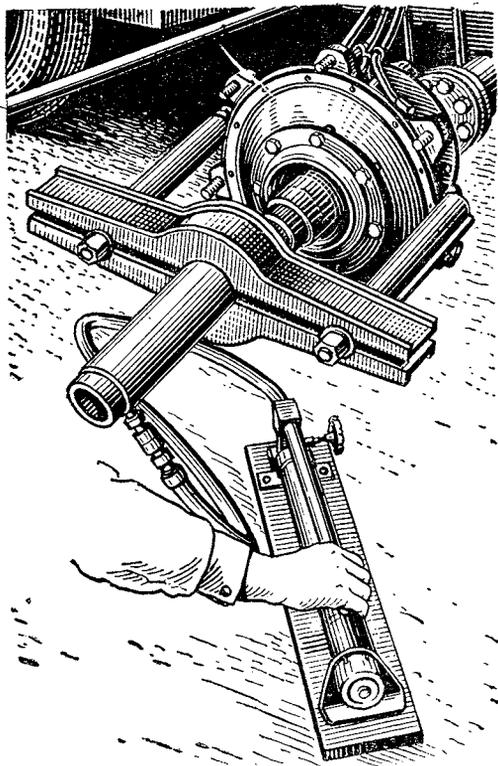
Спрессовка ступицы колеса универсальным приспособлением УК-2А и гидравлическим прессом ГП-20
